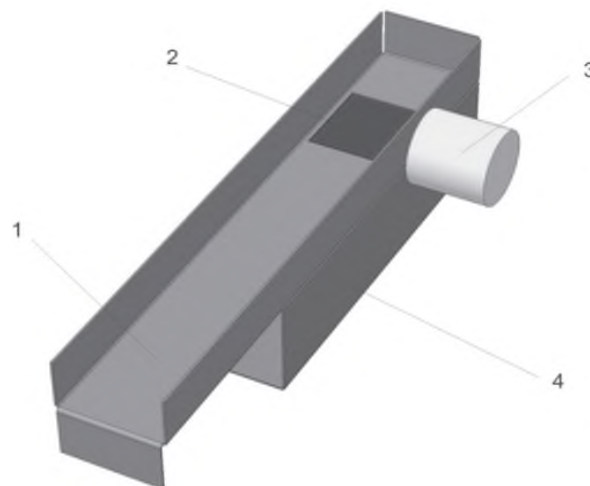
Схема сортировочного механизма: 1 - верхний лоток; 2 - крышка; 3 - электромагнит; 4 - нижний лоток
